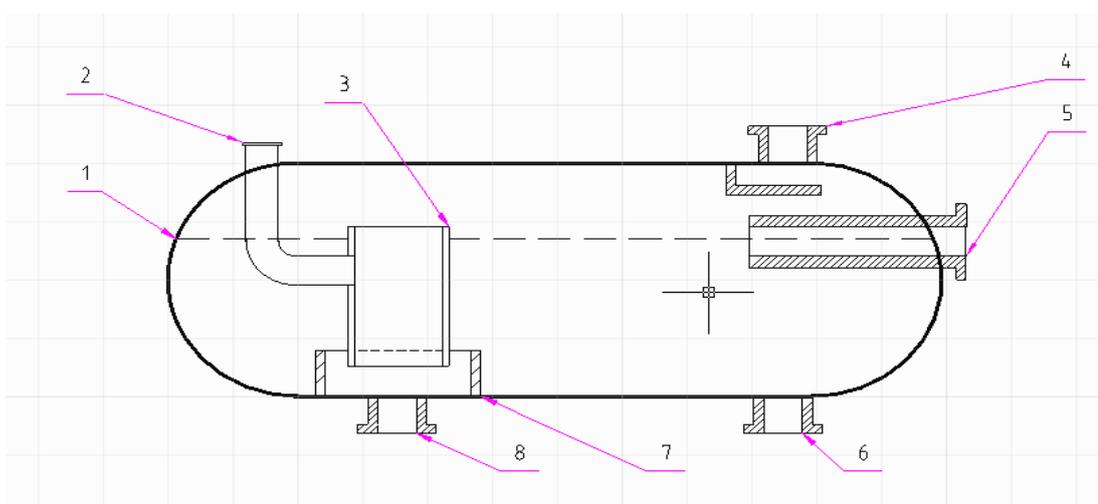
Трёхфазный сепаратор: 1 – резервуар горизонтальный; 2 – патрубок для подачи эмульсии; 3 – вертикальный патрубок; 4 – патрубок выхода газа; 5 – патрубок выхода нефти; 6 – патрубок выхода воды; 7 – стакан дренажа механических примесей; 8 – патрубок вывода шлама
